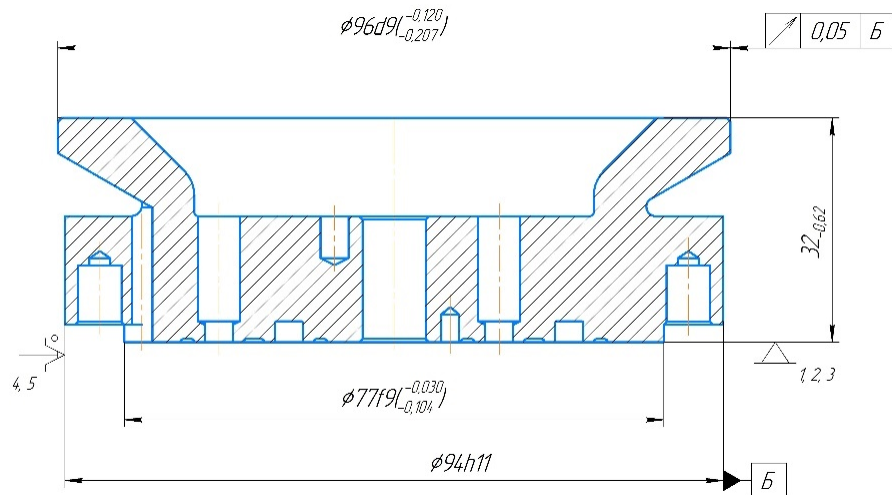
Схема базування та закріплення деталі на операції контролю
